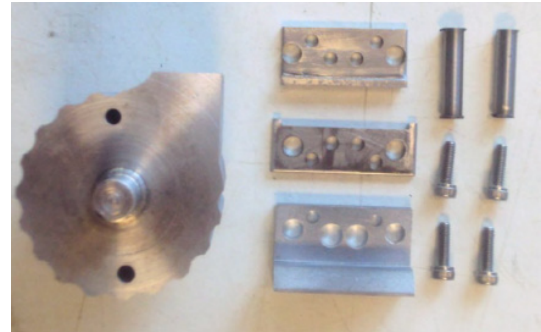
Ensamblaje parte superior del conformador de bumps
